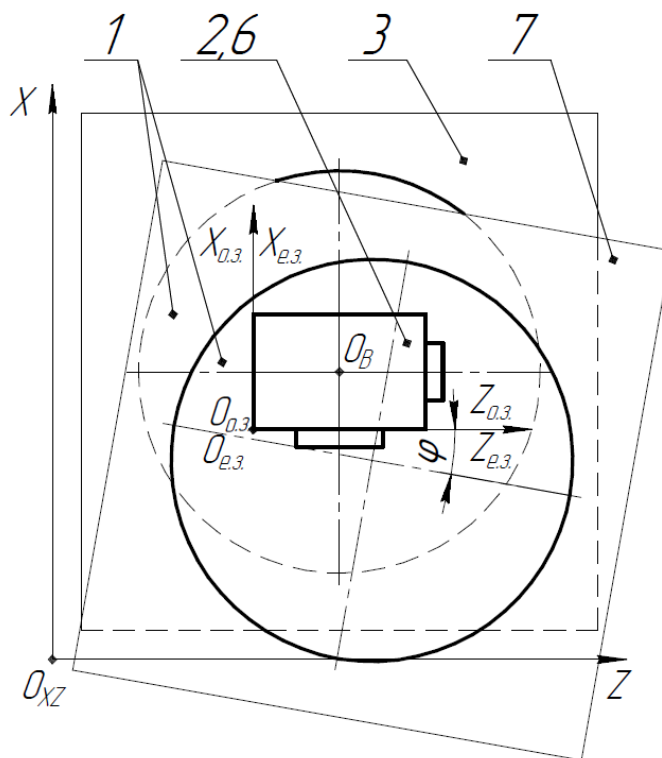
Суміщене зображення положень еталонної та оброблюваної заготовок зі співпадаючими системами координат в горизонтальній площині XZ, отримане поворотом та зсувом цифрової фотографії оброблюваної заготовки відносно цифрової фотографії еталонної заготовки
